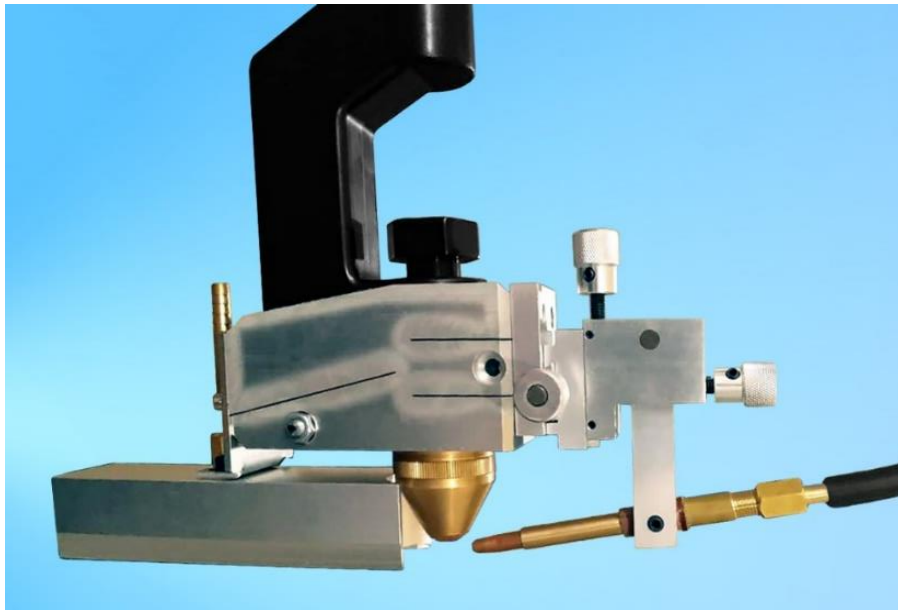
Плазмотрон для зварювання PWM-300 з соплом додаткового газового захисту та системою позиціонування положення присадкового дроту відносно зварювальної ванни.
